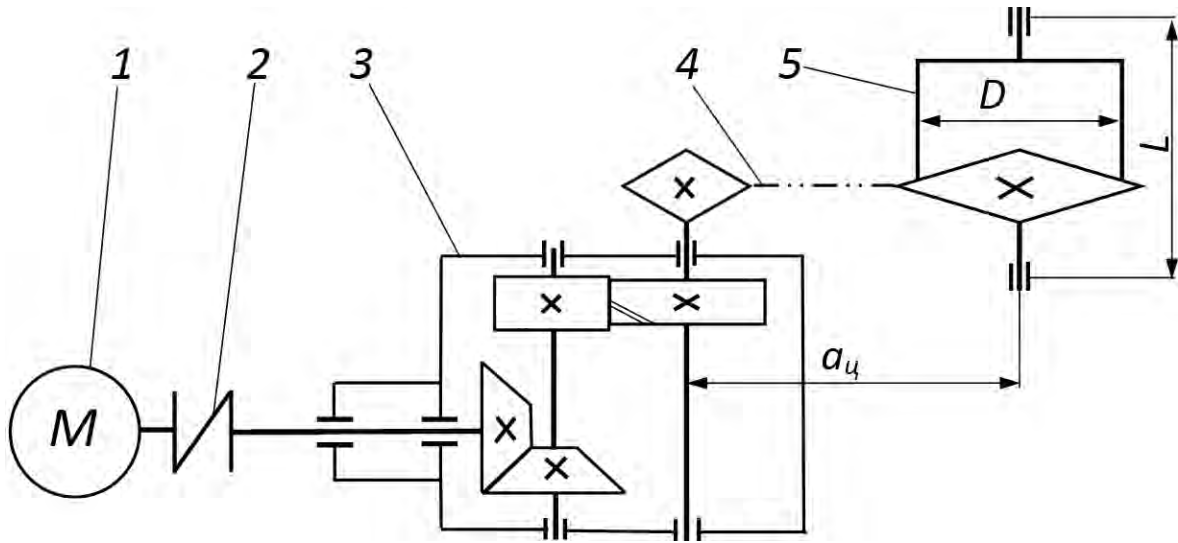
Схема привода подъемно-тягового устройства (вид сверху): 1 – асинхронный электродвигатель; 2 – муфта упругая втулочно-пальцевая; 3 – редуктор коническо-цилиндрический с конической зубчатой передачей с круговым зубом и цилиндрической косозубой зубчатой передачей; 4 – цепная передача; 5 – приводной вал с барабаном
